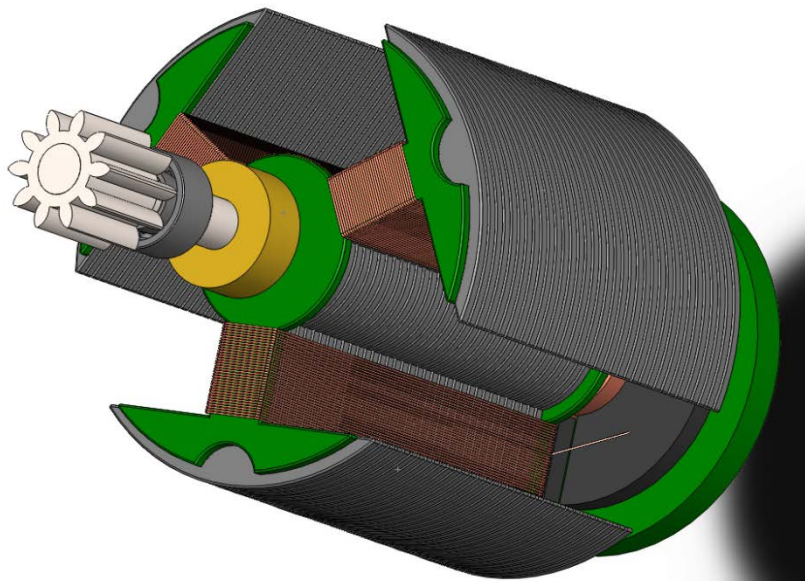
Vista del rotor laminat i la bobina que el magnetitza. (Font: Pròpia amb SolidWorks)
